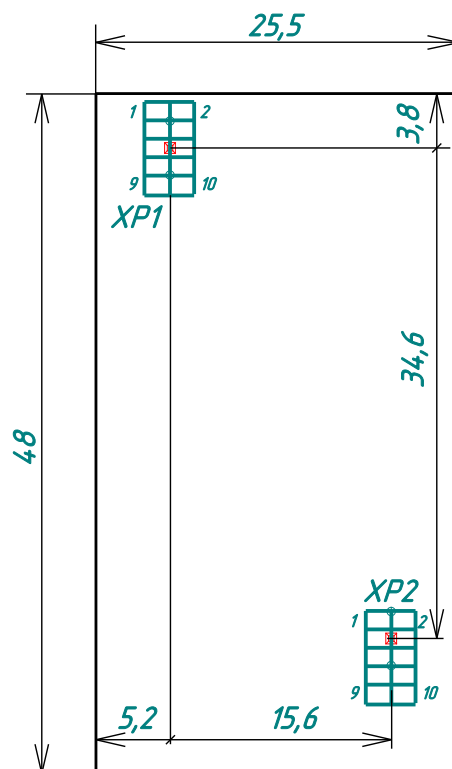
габаритные и установочные размеры модуля AD-RMA-MP
